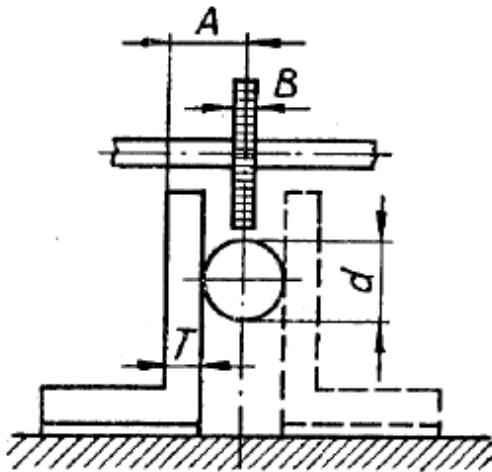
Фрезерування відкритої шпонкової канавки
